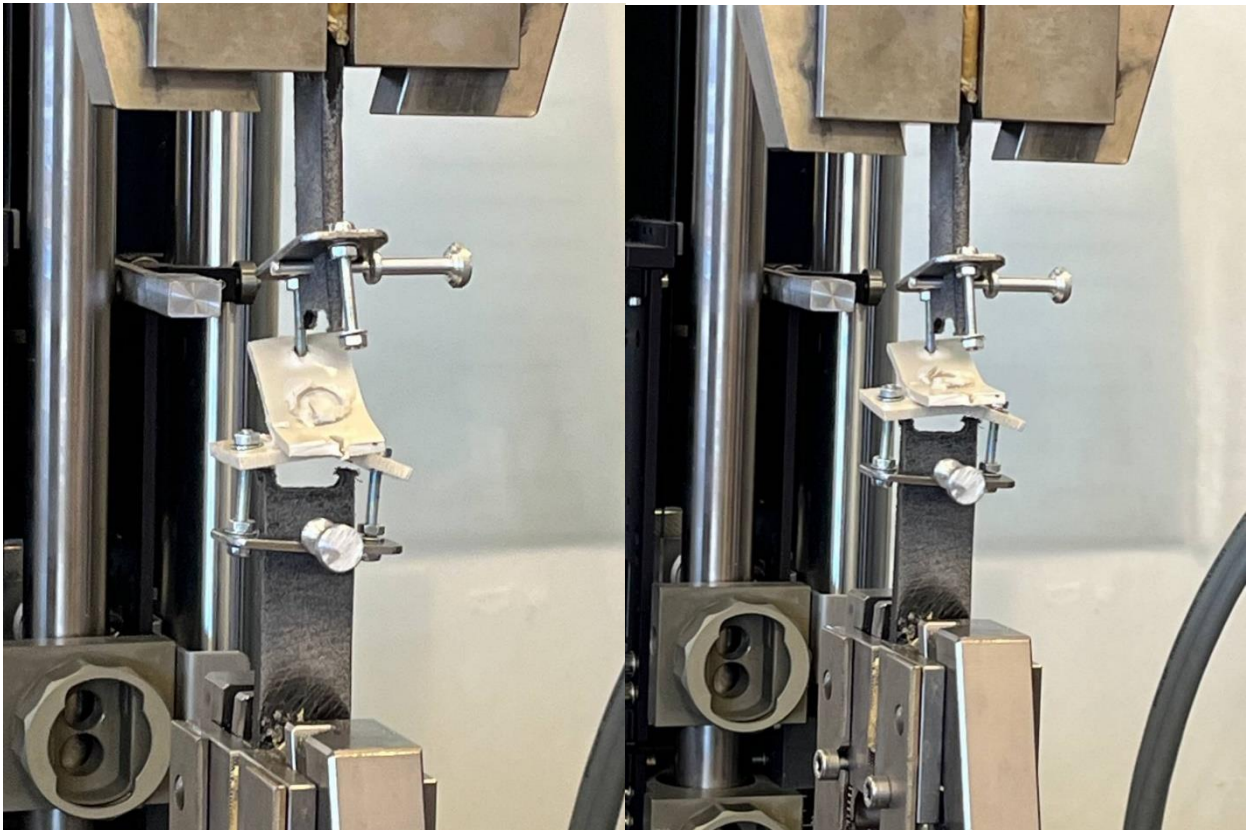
Образцы сварного соединения полипропилена в момент разрушения
